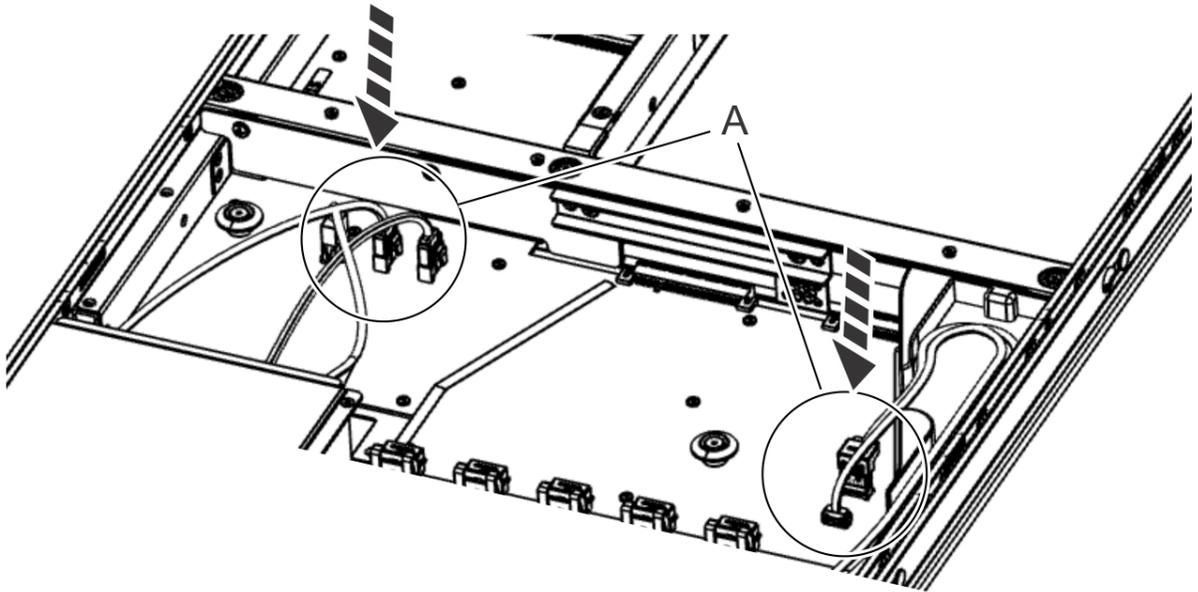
Kabel wieder an die Stromverteilerplatte anschließen
